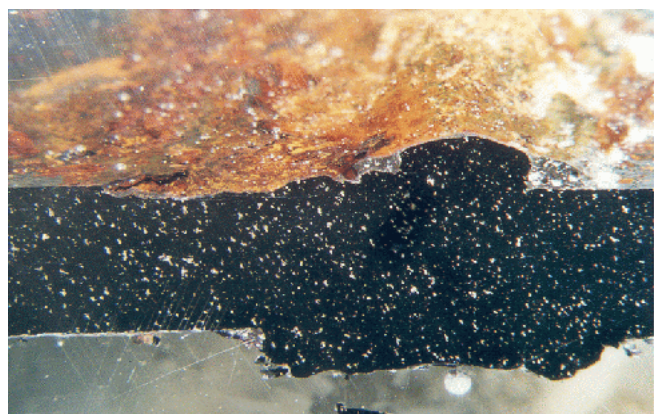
Muldenkorrosion entlang der Schweißnahtkante, Vergrößerung 8x
